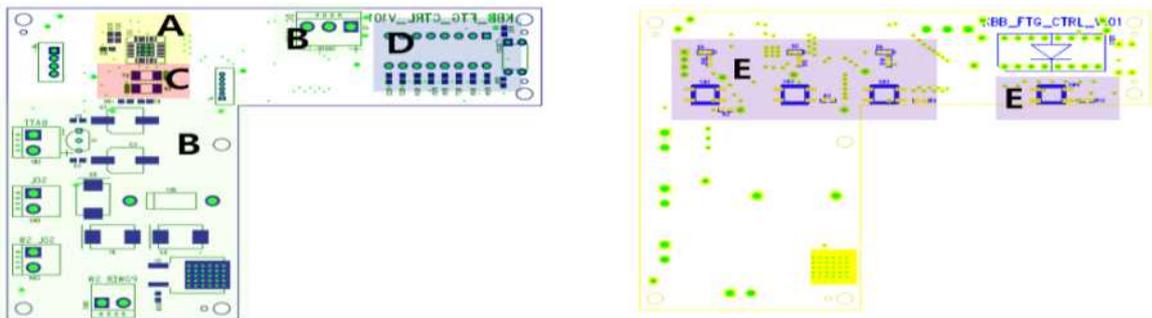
메인보드 PCB 회로도 (좌:앞면; 우:뒷면)
